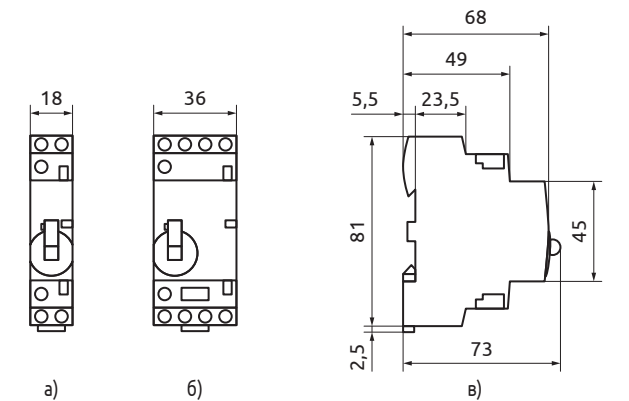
Габаритный чертеж контакторов АСМ-М на токи от 16 до 25 А:
